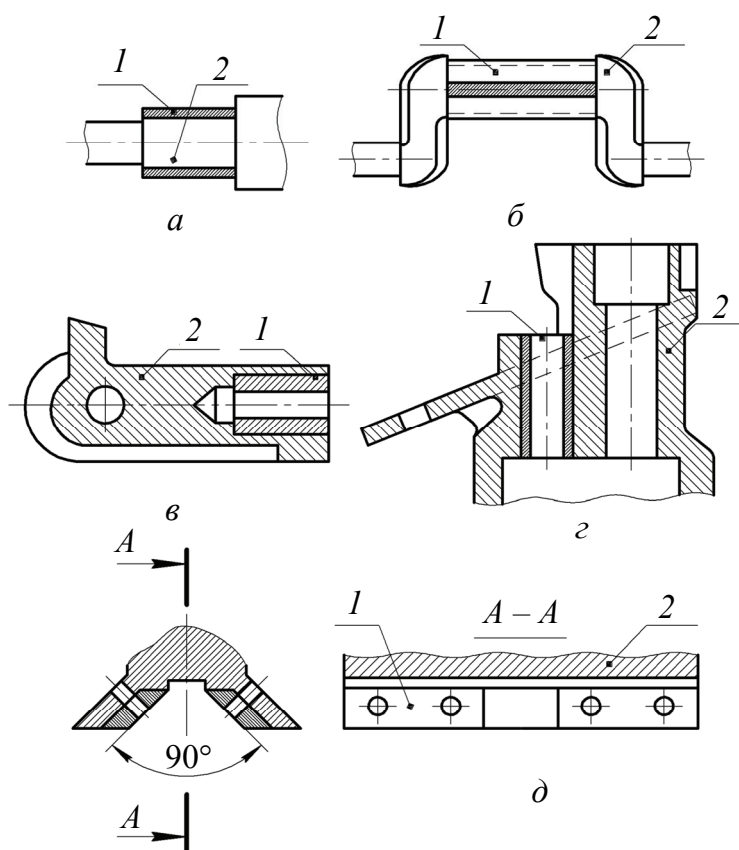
Типовые случаи применения дополнительных деталей при ремонте: а – установка на валу втулки; б – установка полувтулки на шейке коленчатого вала; в – установка втулки с резьбой; г – установка втулки в отверстие; д – установка планки на износившейся плоскости; 1 – деталь-компенсатор; 2 – ремонтируемая деталь
